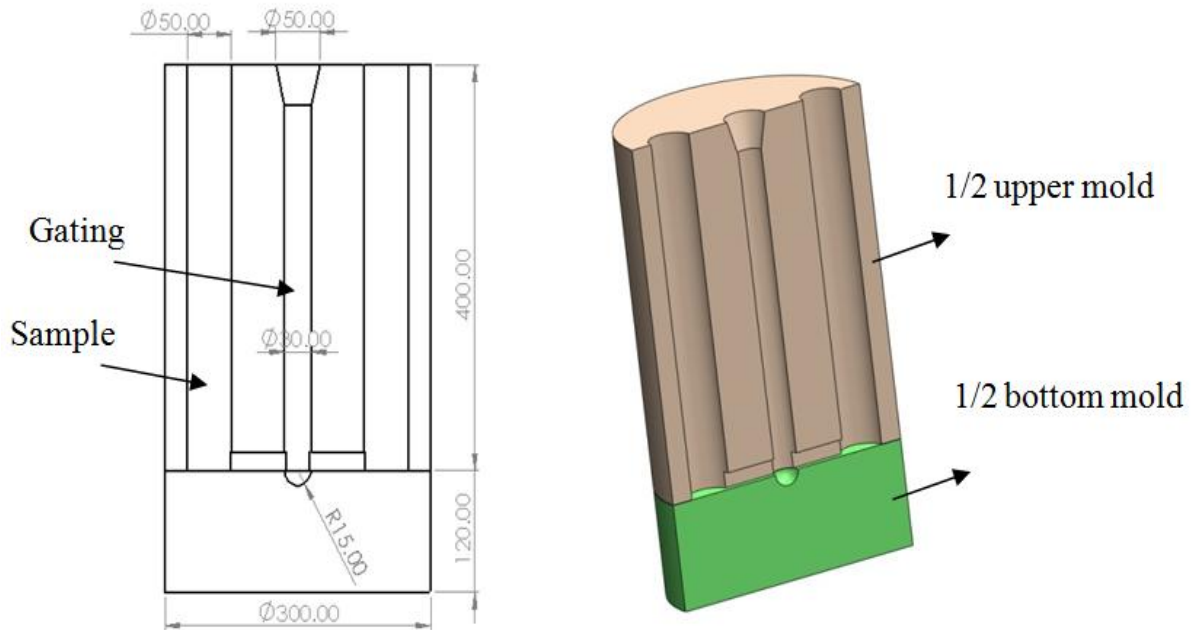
Croquis de coulée des éprouvettes. Dimensions en millimètres.
